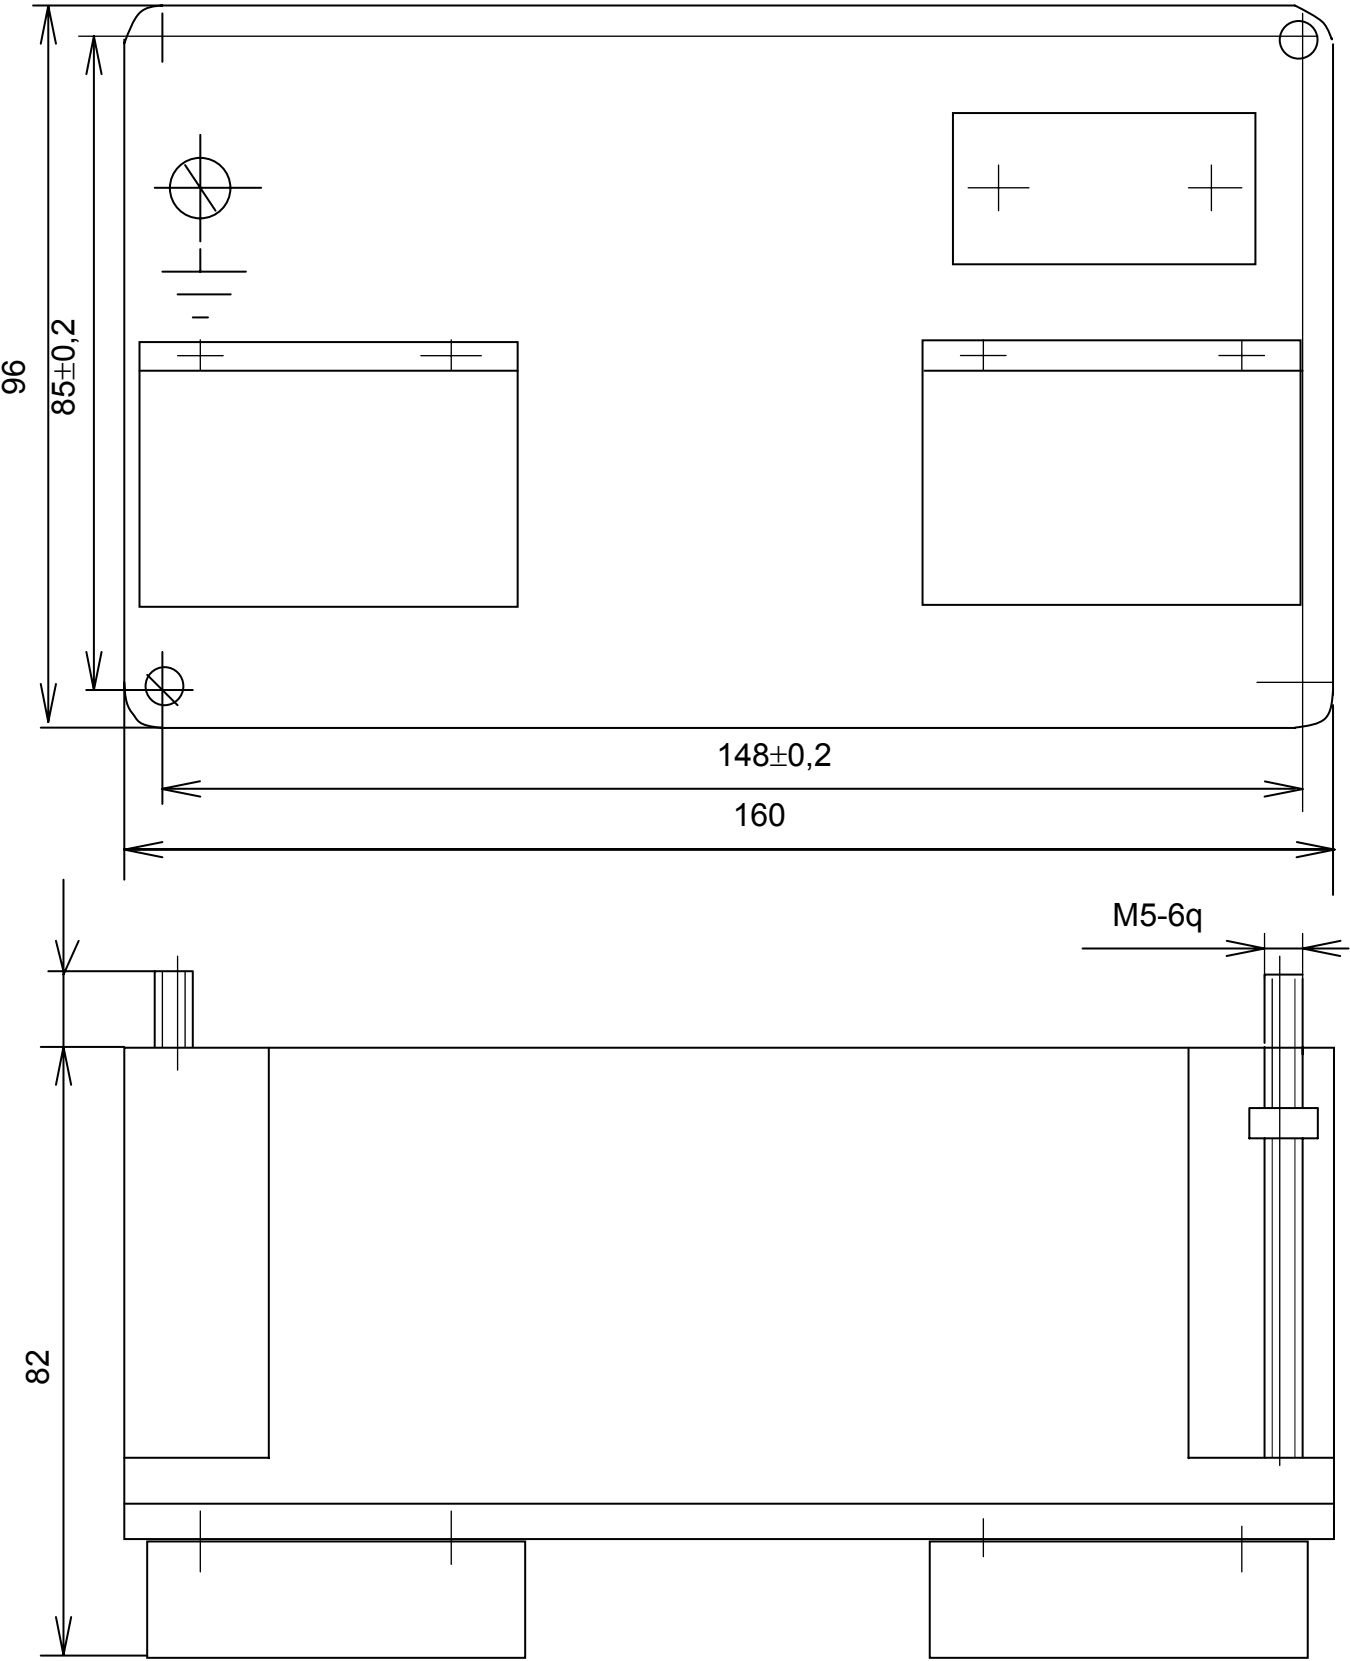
Общий вид и габаритные и присоединительные размеры блока датчика БСПТ-10МШ
